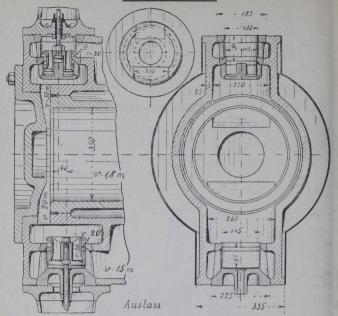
Ventilsteuerung für 350 mm Cylinderdurchmesser.
